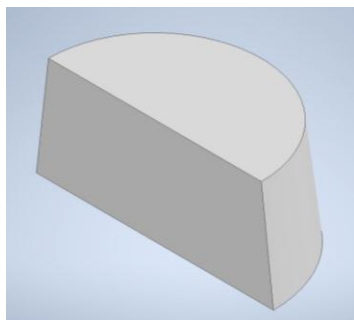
3Д-модель деталі “Платформа камери”
